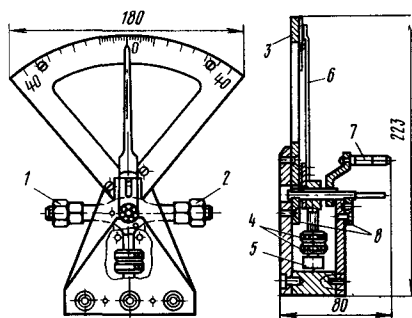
Прибор для балансировки рычага с грузами всережимного регулятора:
